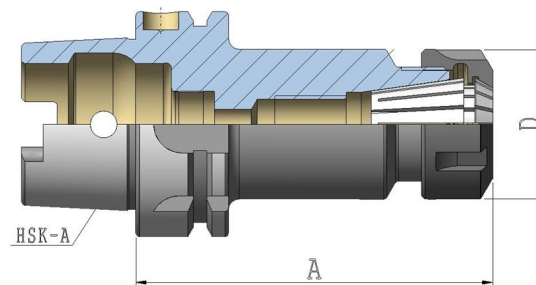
Referenzwerkzeugaufnahme mit HSK63 Typ A zur Ankopplung an die Spindel (linke Seite) und Spannzangenaufnahme ER40 zur Aufnahme der Fräser (rechte Seite), Zeichnung entnommen aus [San18]
